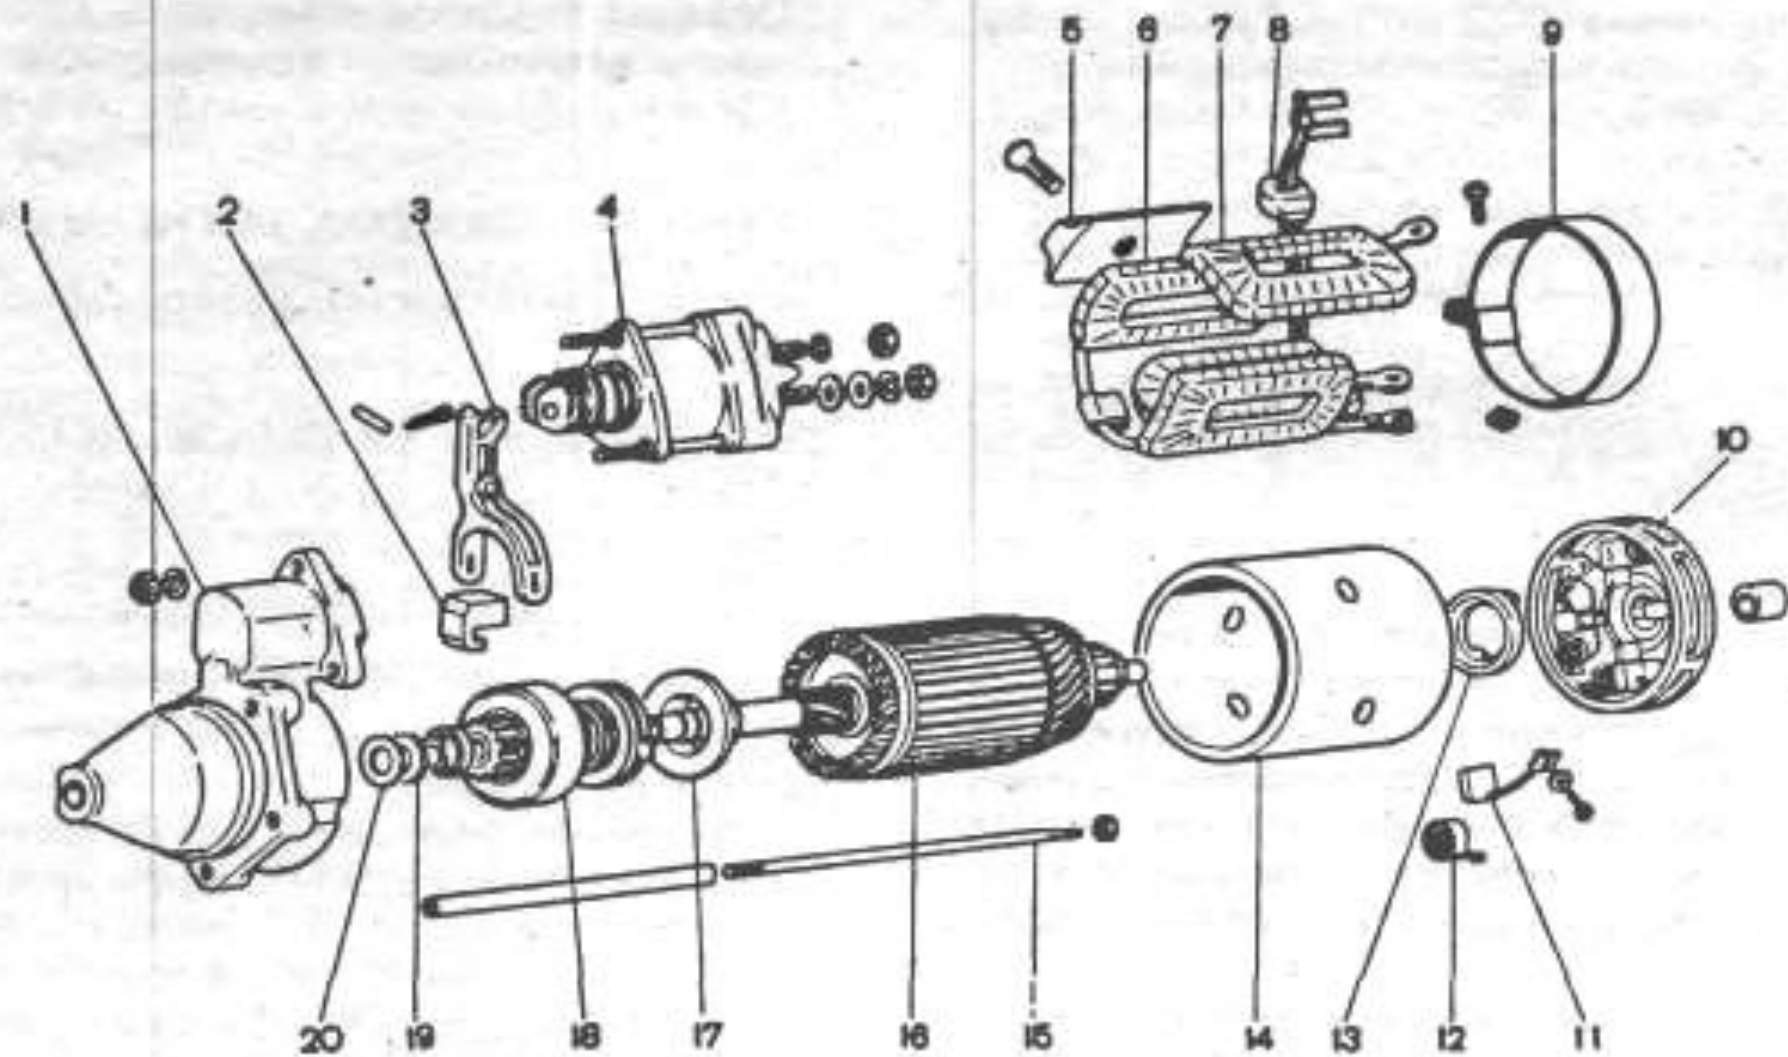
Детали стартера: 1 - крышка стартера со стороны привода; 2 - резиновая заглушка; 3 - рычаг привода; 4 - тяговое реле; 5 - полюс статора; 6 - серийная обмотка статора; 7 - шунтовая обмотка статора; 8 - резиновая заглушка; 9 - защитная лента; 10 - крышка со стороны коллектора; 11 - щетка; 12 - пружина щетки; 13 - тормозной диск крышки; 14 - корпус; 15 - стяжная шпилька; 16 - якорь; 17 - ограничитель хода шестерни; 18 - обгонная муфта с шестерней привода; 19 - упорная шайба; 20 - регулировочная шайба
